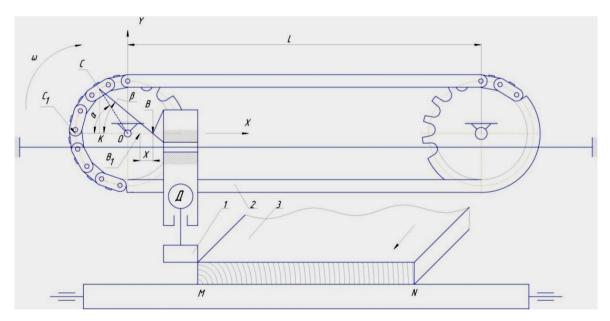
Схема реализации работы цепного привода при обработке горизонтальных поверхностей: 1 – режущий инструмент; 2 – цепной привод; 3 – обрабатываемый материал
